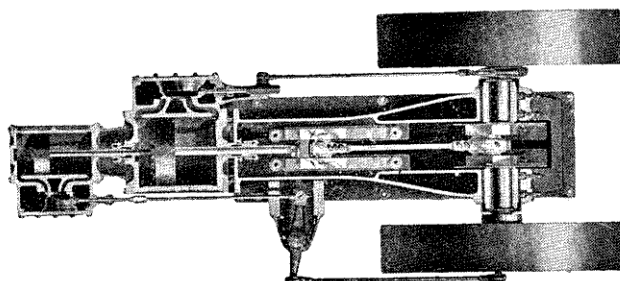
Coupe en plan du moteur compound SKINNER.
